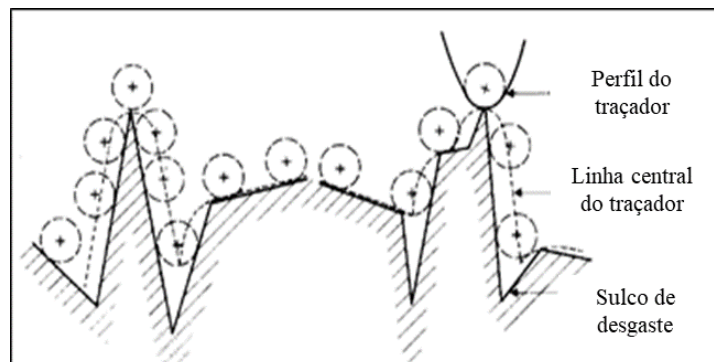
Representação da variação entre a superfície real e a superfície captada por um apalpador (adaptado de BUSHAN [1]).
